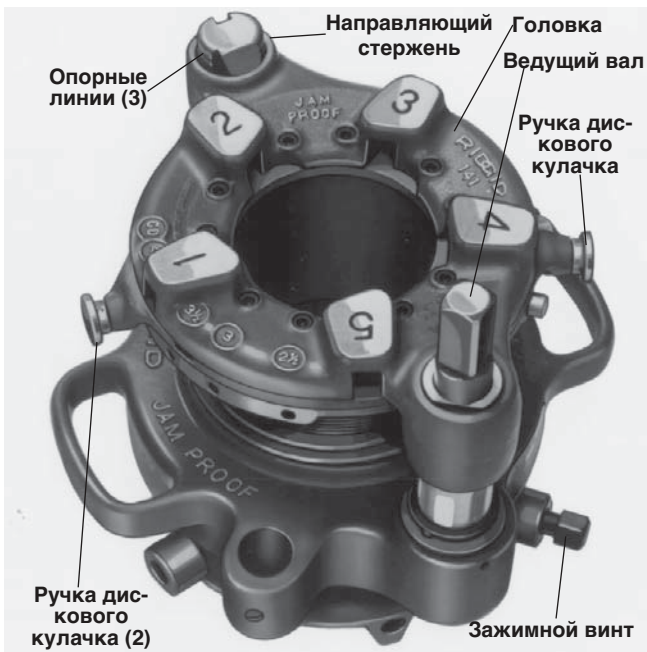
Головка № 141 с зубчатой передачей с опорными линиями зубчатой втулки и направляющего стержня
